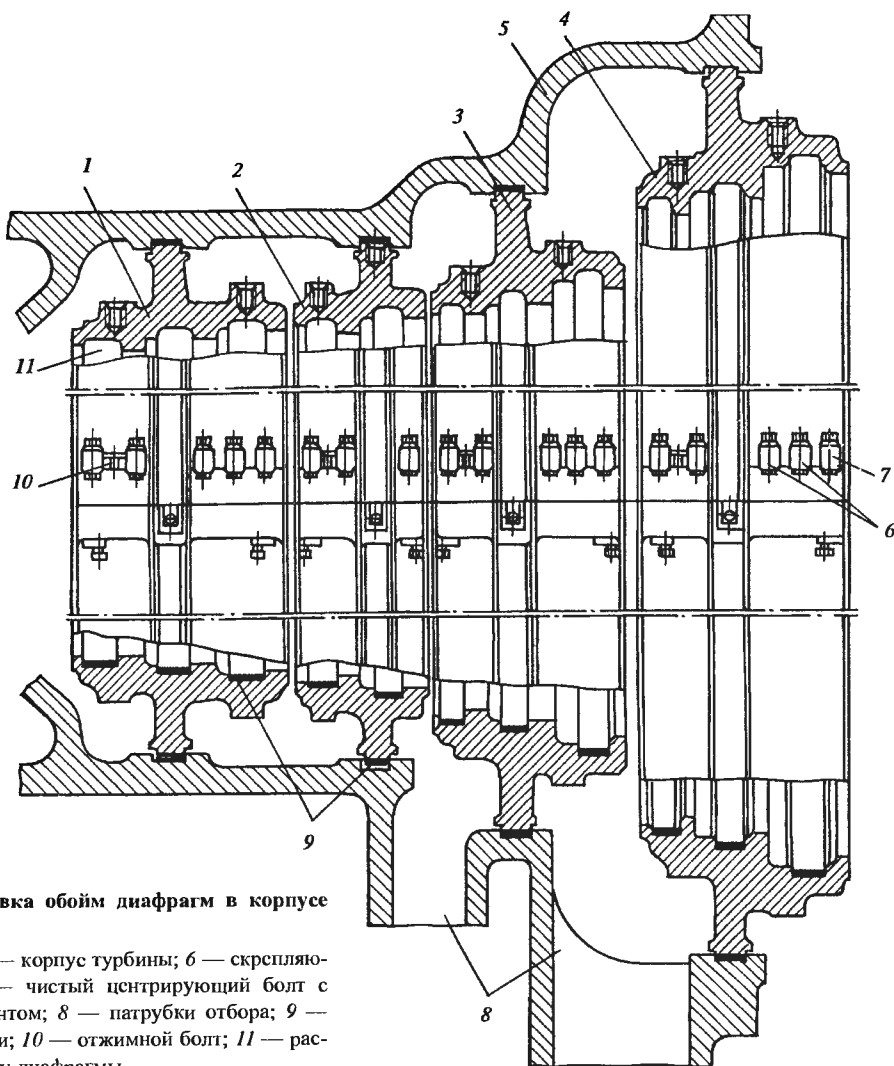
Установка обойм диафрагм в корпусе турбины:
